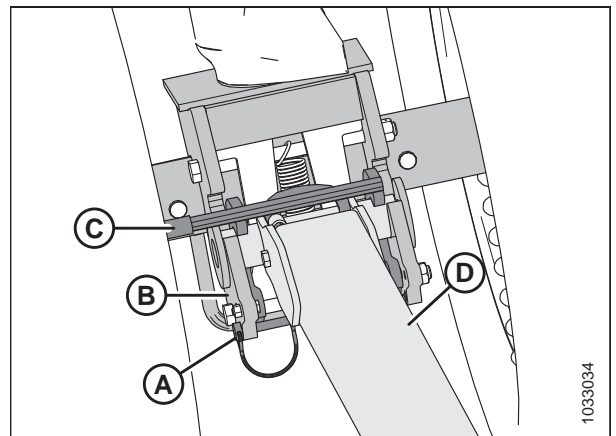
Удлинитель буксирной тяги и транспортный шарнир
